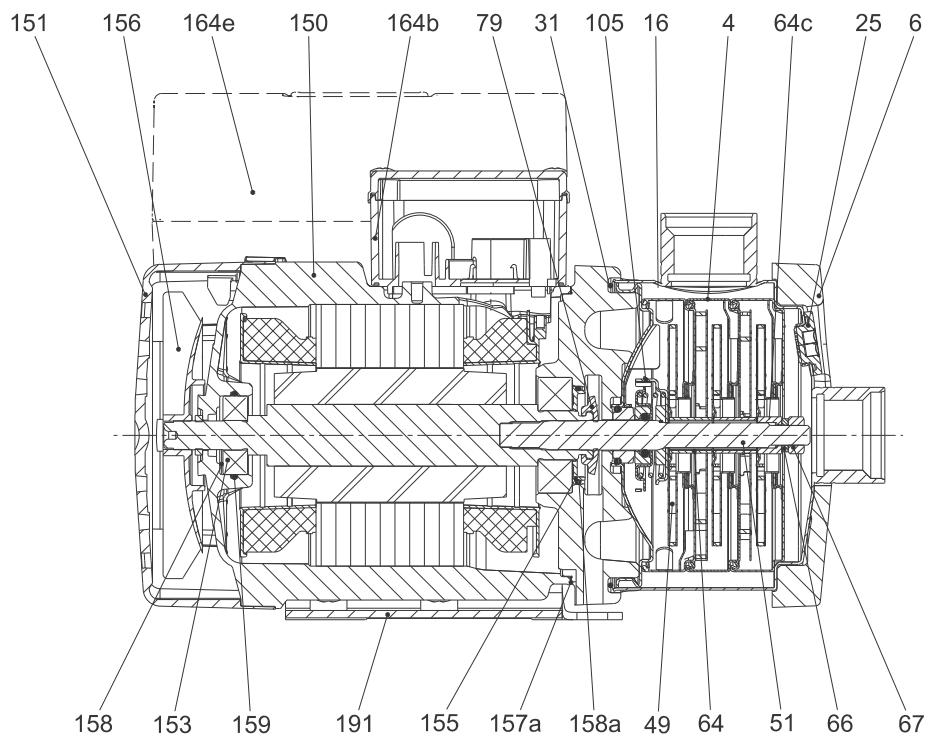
CM, CME 1-3 s motorem MG, MGE 71
